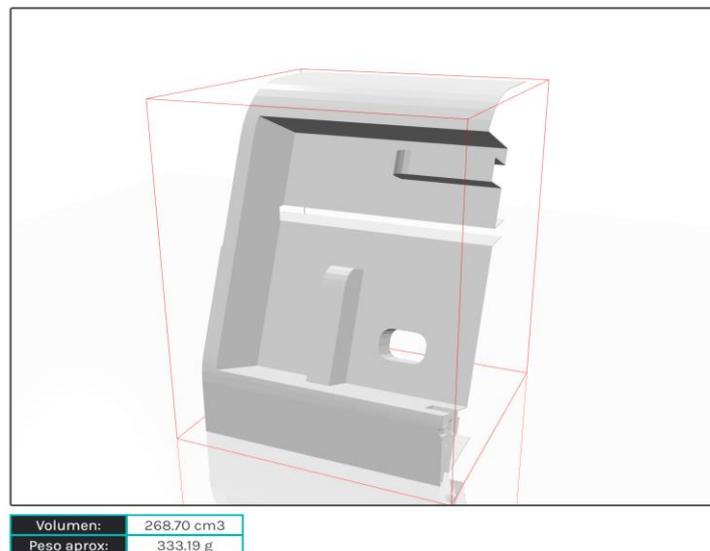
calculando el coste de impresión 3D. Fuente: imprimakers.com
